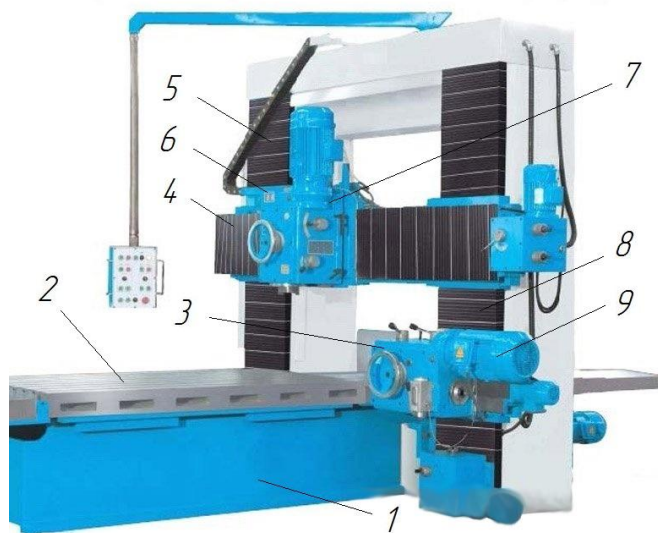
Двухстоечный продольно-фрезерный станок
